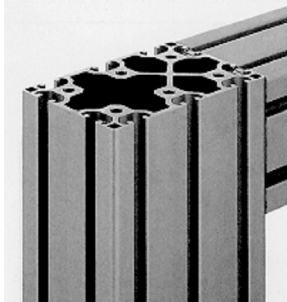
mfZ) Auch in der Verbindungstechnik und für Messebau sind Strangpressprofile gut geeignet
